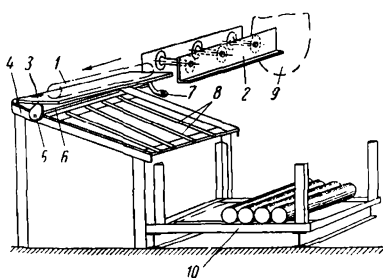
Скат-рольганг для спуска в тару отрезаемых на пиле заготовок
